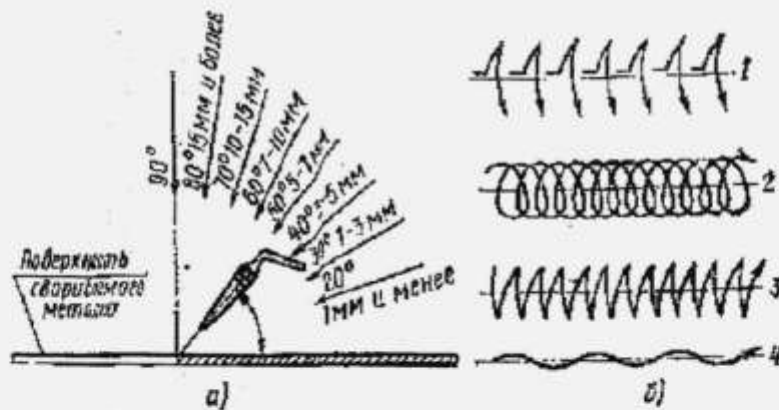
Углы наклона мундштука горелки при сварке
